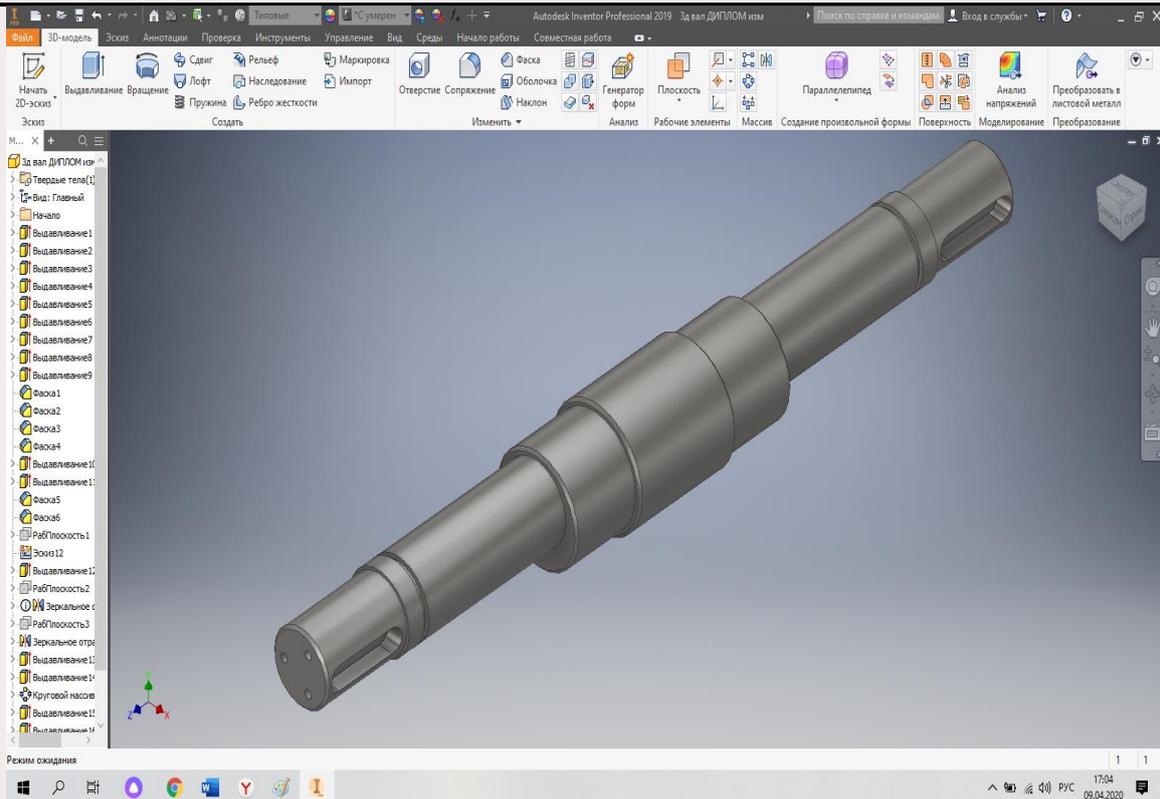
3D модель эксцентрикового вала щековой дробилки
